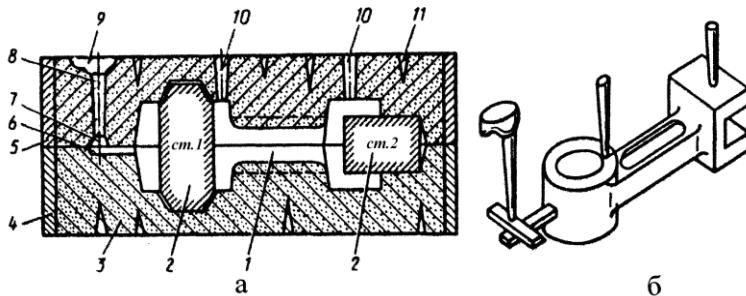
Эскизы собранной литейной формы (а) и готовой чугунной отливки с литниковой системой (б): 1 – полости формы; 2 – стержни; 3 – формовочная смесь; 4, 5 – нижняя и верхняя опоки; 6 – питатель; 7 – шлакоуловитель; 8 – стояк; 9 – литниковая чаша; 10 – выпор; 11 – газоотводящие каналы
